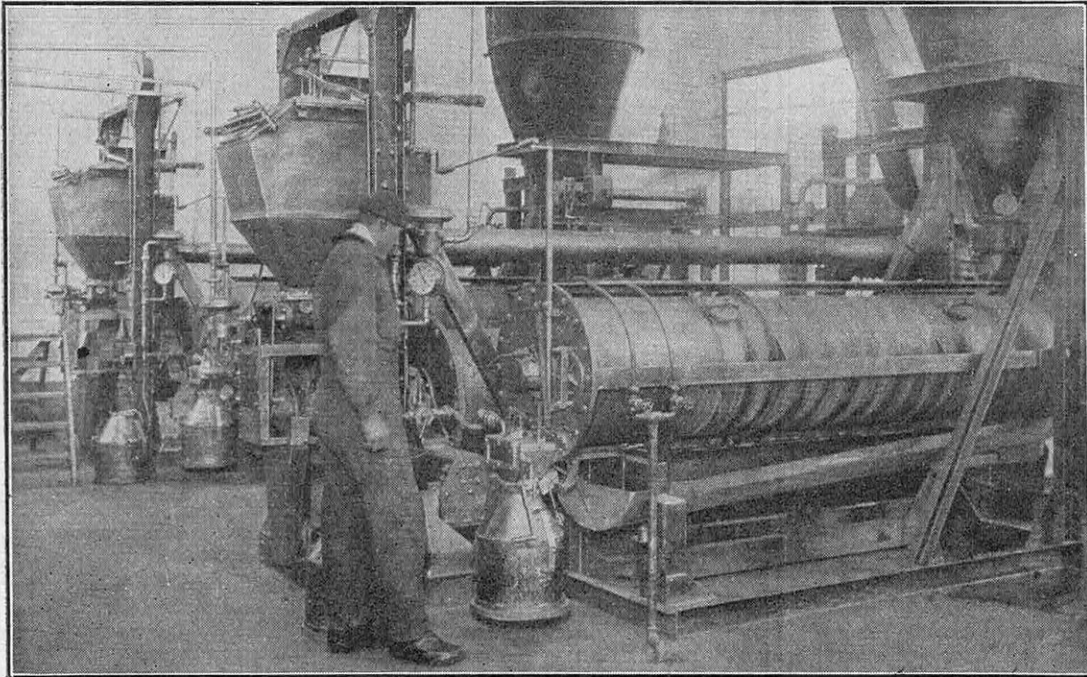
MACHINE A BROYER ET A POLIR LA POUDRE D'ALUMINIUM
